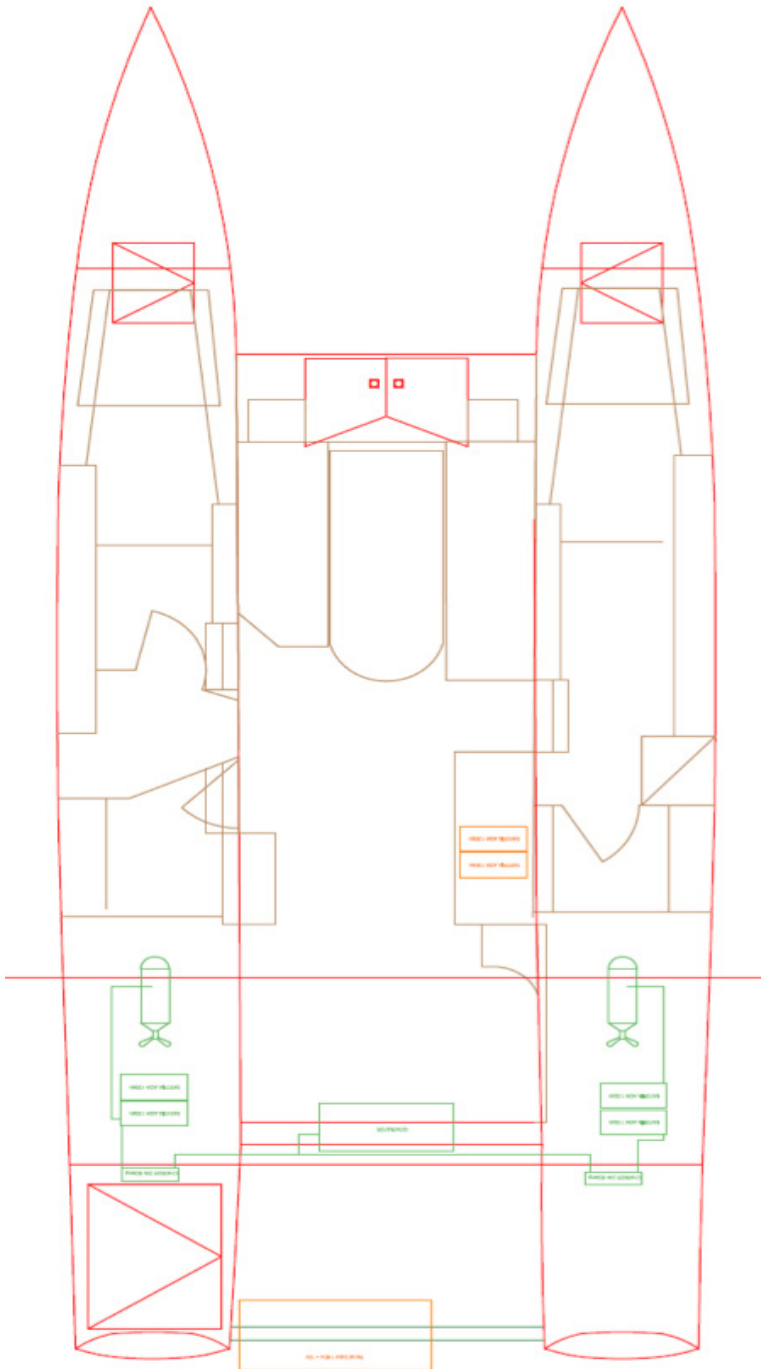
Plano en planta AutoCAD. Distribución interior y diseño de la instalación. Fuente: propia
